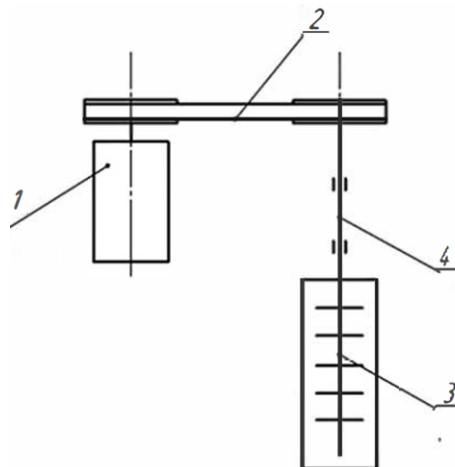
Кінематична система : 1 – двигун; 2 – пасова передача; 3 – ротор; 4 – підшипниковий вузол
